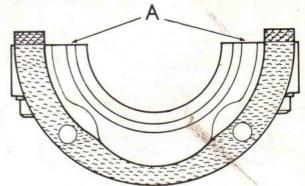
JOINT DE COQUILLE DE RETOUR D'HUILE
